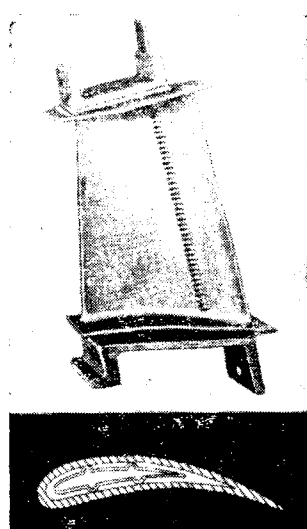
Сопловая лопатка второй ступени турбины двигателя Р-100
